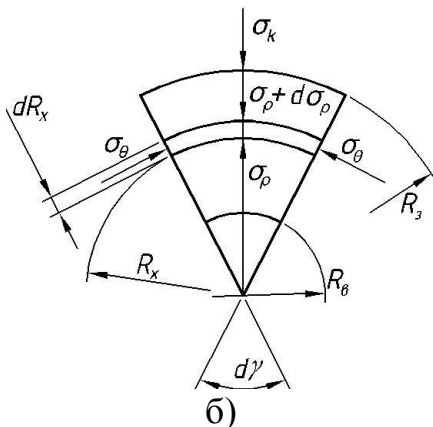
Розрахункова схема для визначення зусилля деформації заготовки шнека:
